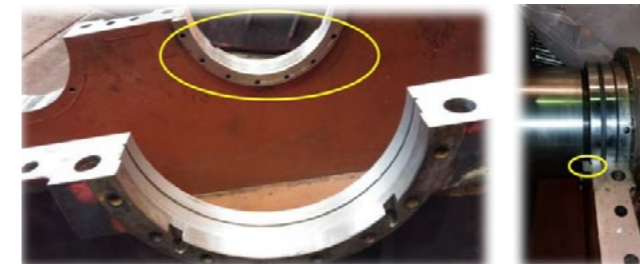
Gövdede Flanşın Oturacağı Yerin İşlenmesi
